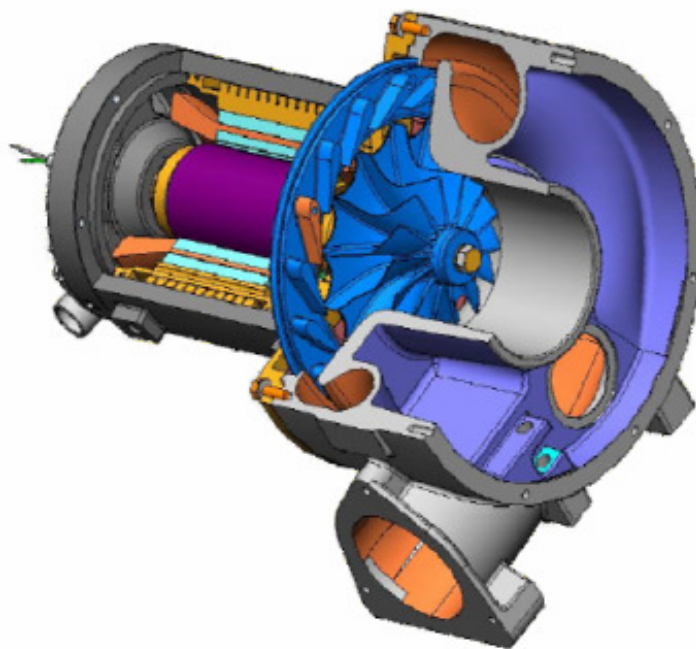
Schéma přepínání pomocí kombinace kompresoru a turbodmychadla [29]
